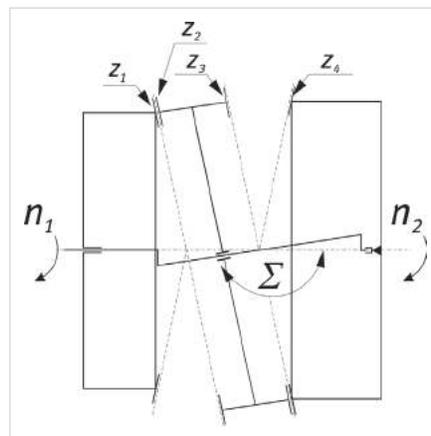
Кинематическая схема редуктора с плоско-конической прецессирующей передачей
